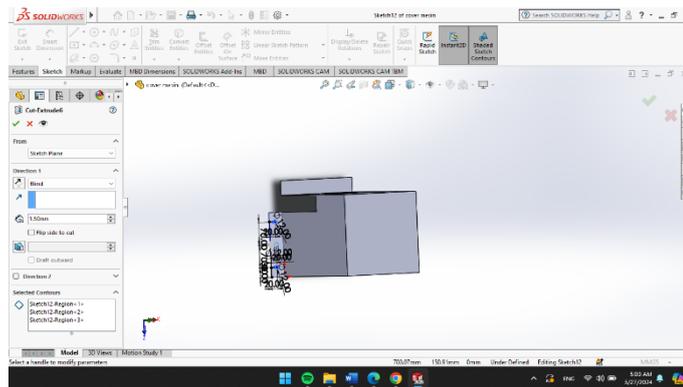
Langkah 3 Penggambaran Cover Mesin
